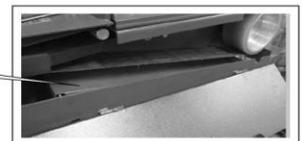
Установка вырубного пресса для труб / ленточно-шлифовального станка.
